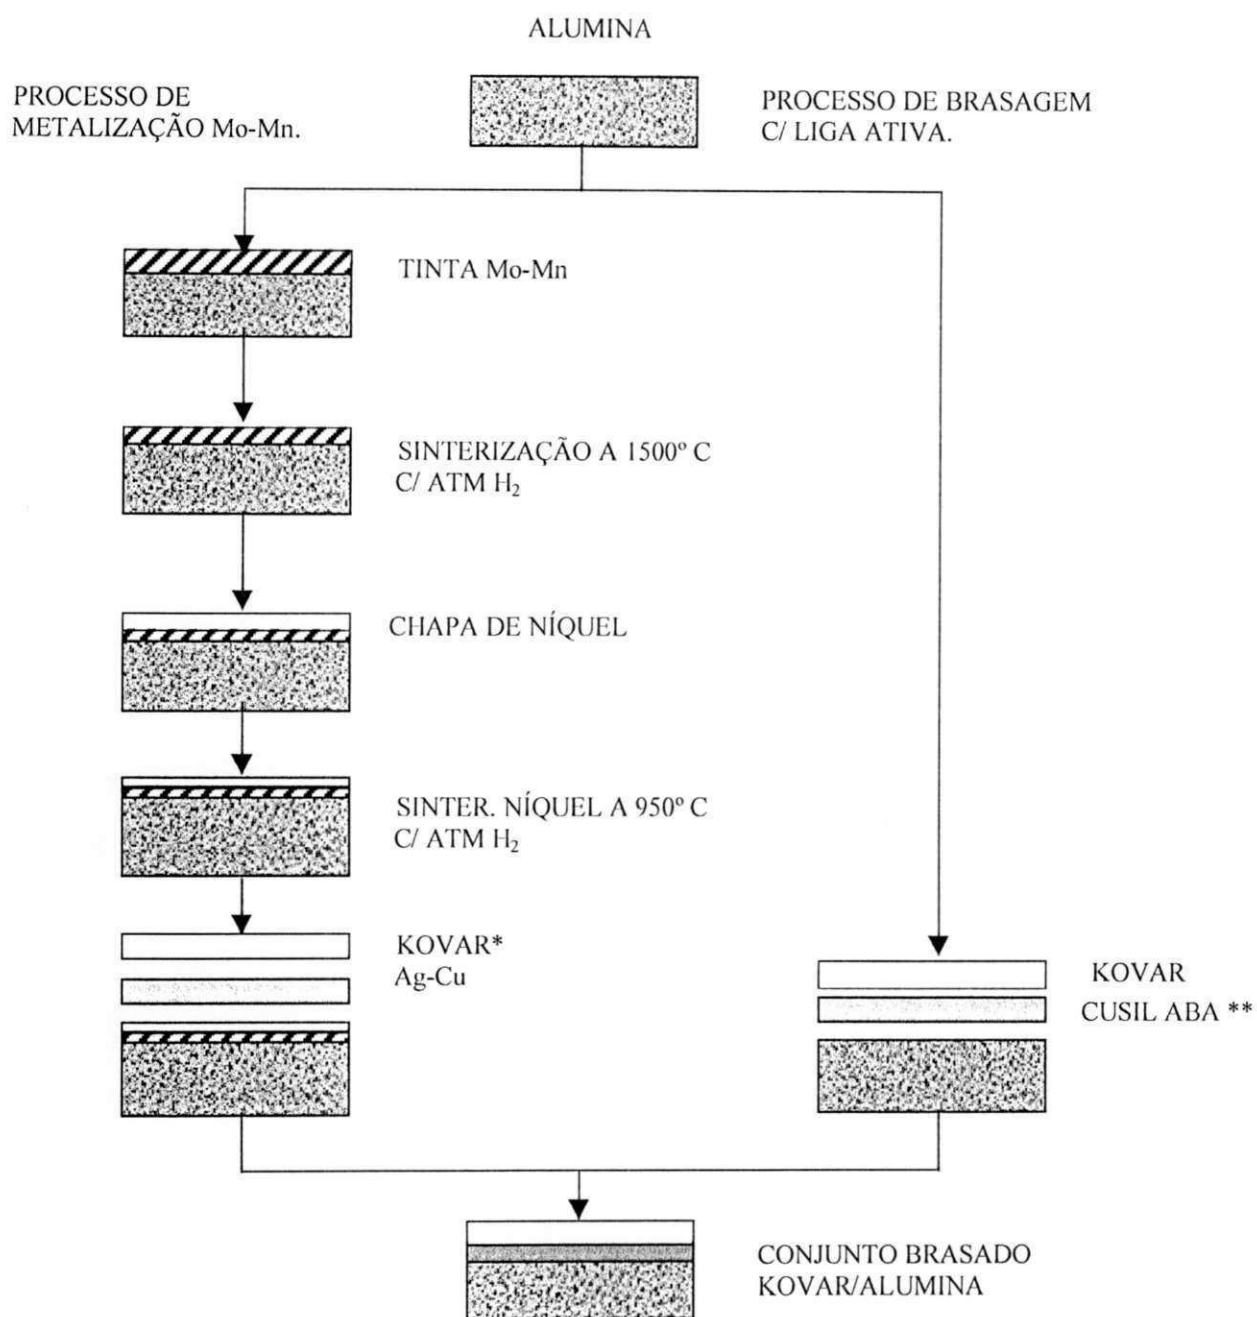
Representação esquemática dos processos de brasagem por metalização Mo-Mn e brasagem com metal ativo (AWS - Welding Handbook, 1991. p.396).
